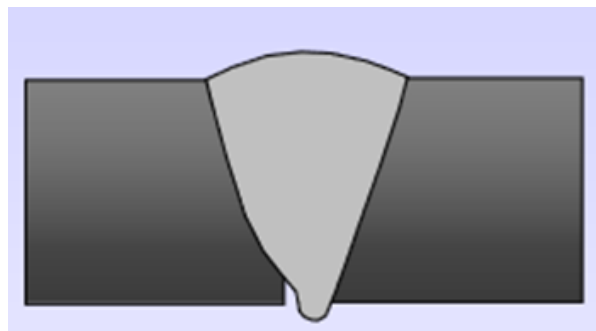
Fuziune rădăcină incompletă. Sursă: M.S. Rogers, Welding Inspection Defects/Repairs Course Reference WIS 5, 2003.
